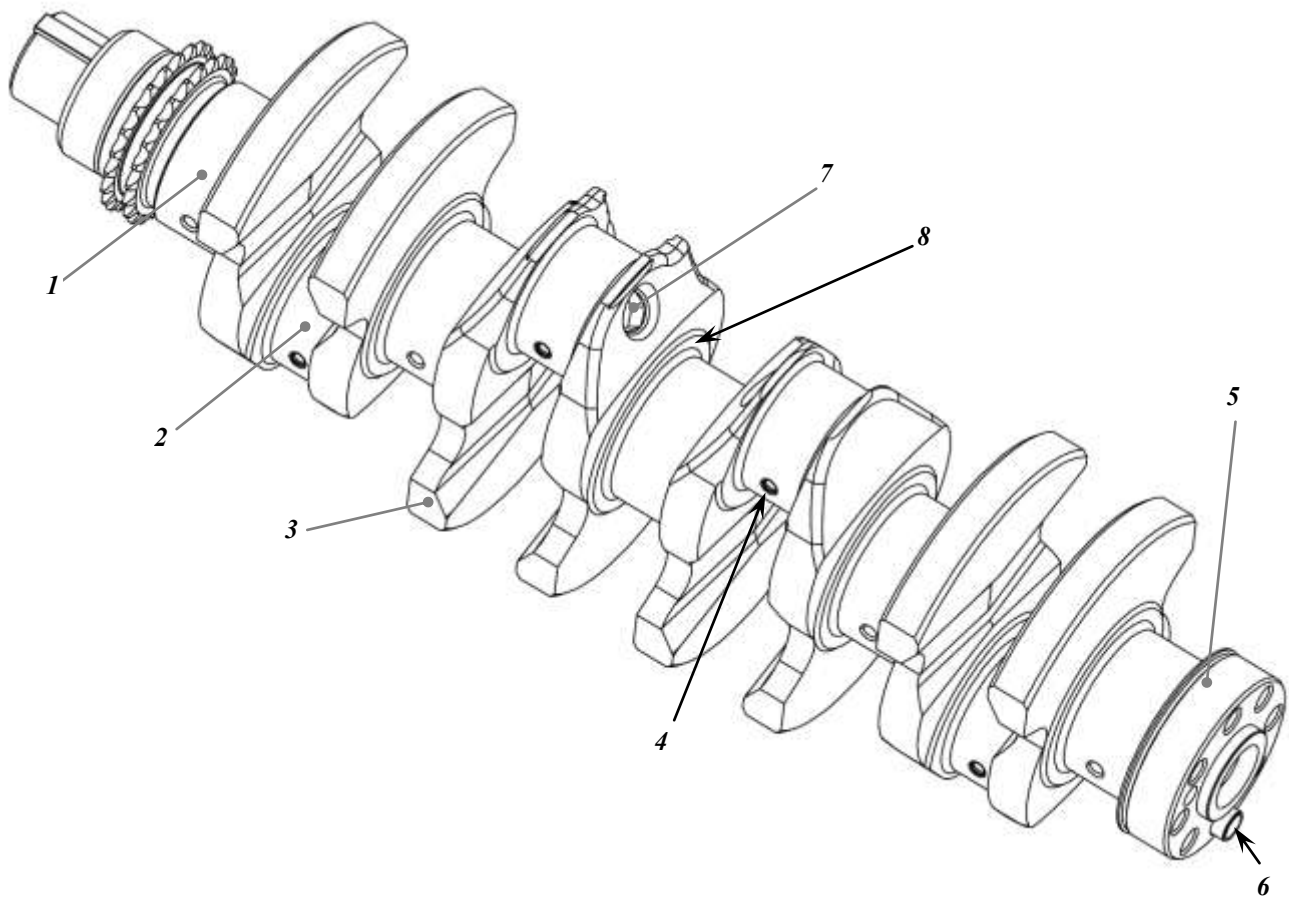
Вал коленчатый в сборе с пробками, установочным штифтом и звездочкой: 1 – 1-я коренная шейка; 2 – 1-я шатунная шейка; 3 – 3-й противовес; 4 – отверстие для подвода масла к 3-му шатунному подшипнику; 5 – шейка под задний сальник; 6 – штифт установочный маховика; 7 – пробка (заглушка) масляного канала; 8 – опорная поверхность под упорный подшипник.
